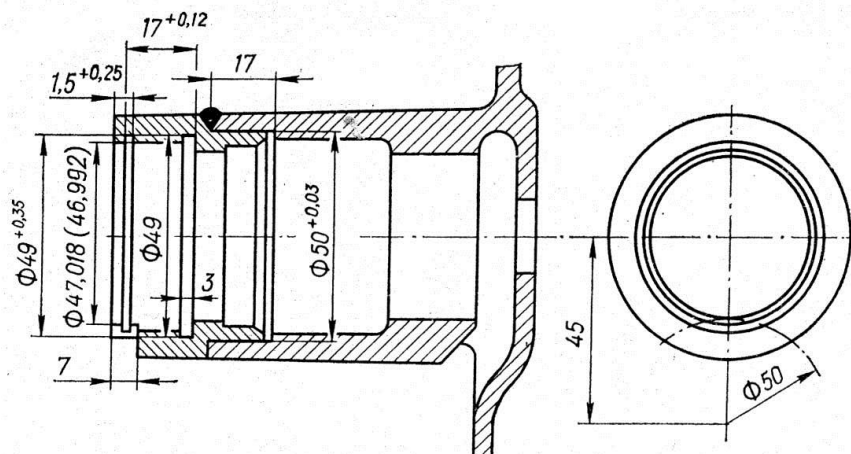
Корпус водяного насоса двигуна типу ЗИЛ, відновлений вставлянням додаткової ремонтної деталі.
